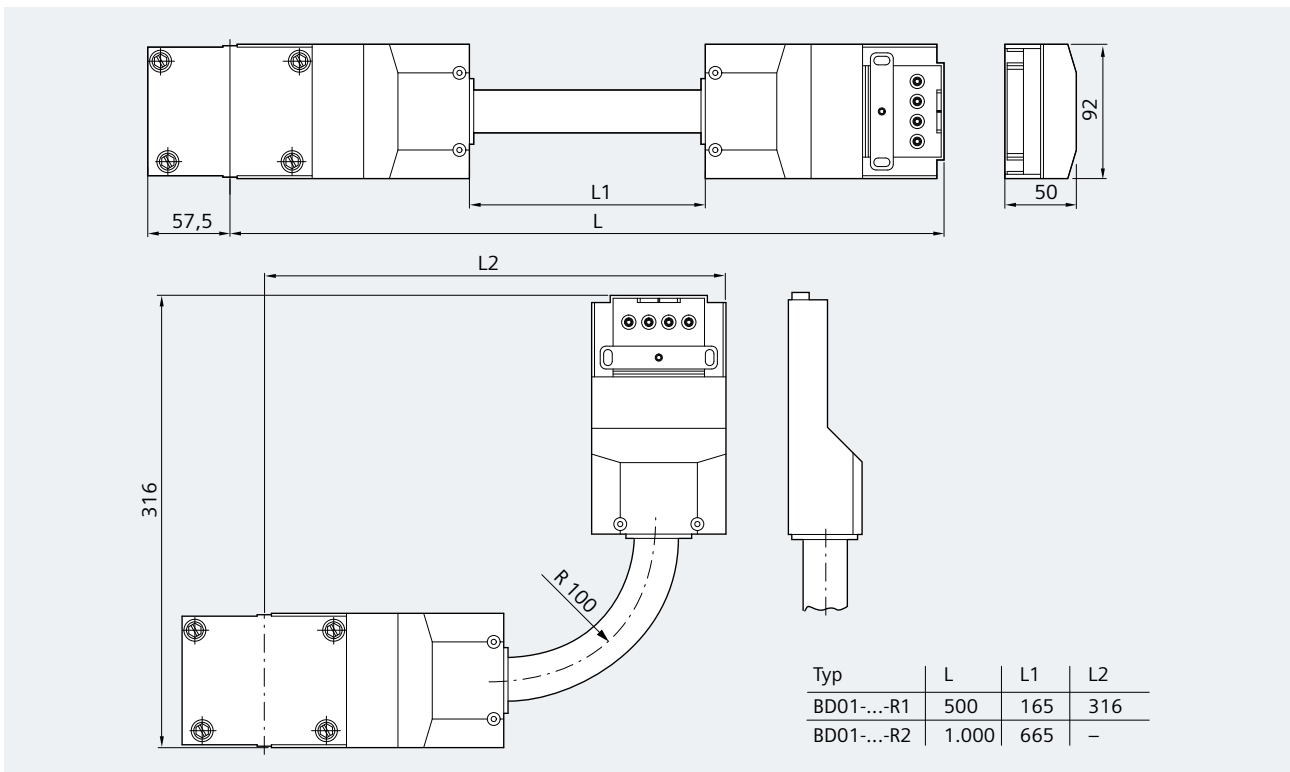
/5: Maßzeichnungen für Richtungsänderungen BD01-R1, BD01-160-R1, BD01-R2 und BD01-160-R2 (Maße in mm)
